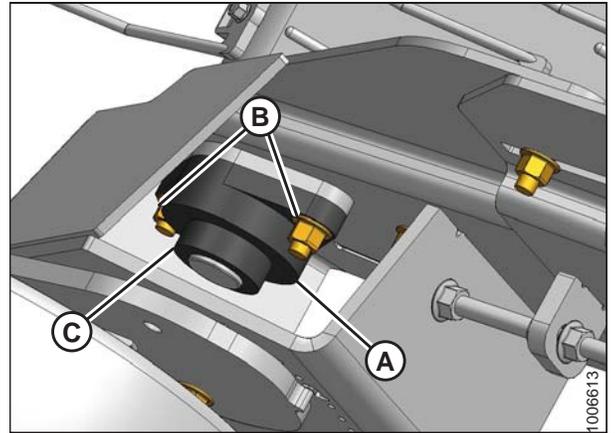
Cama delantera de lado izquierdo; lado derecho opuesto.
